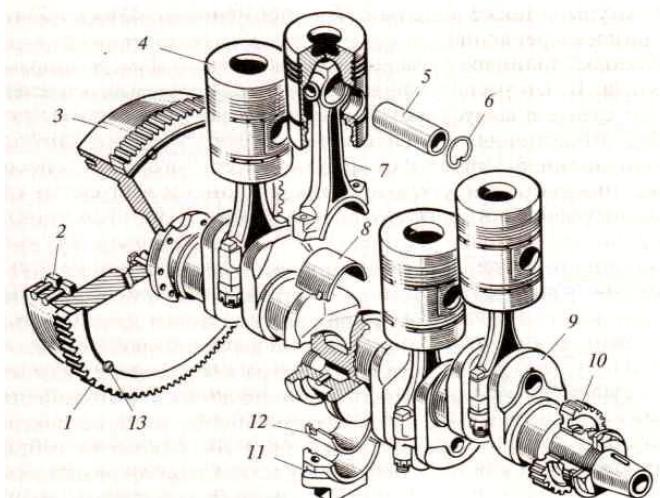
Кривошипно-шатунный механизм рядного двигателя:
